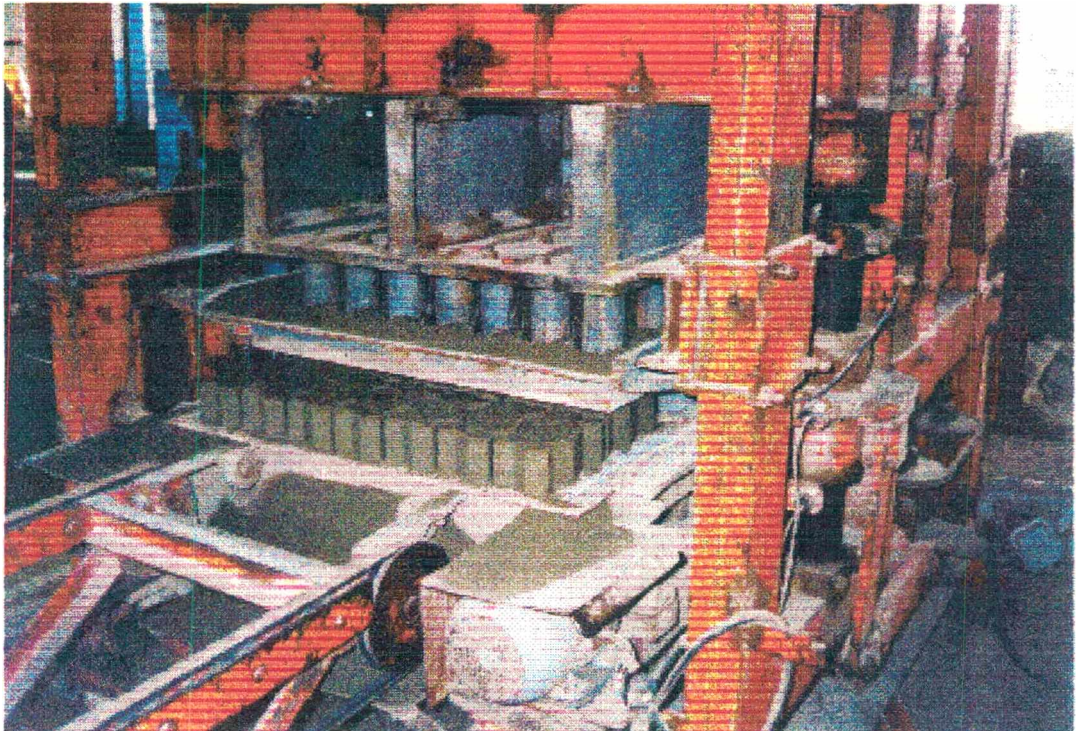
Peças de concreto para pavimentação sendo moldadas
